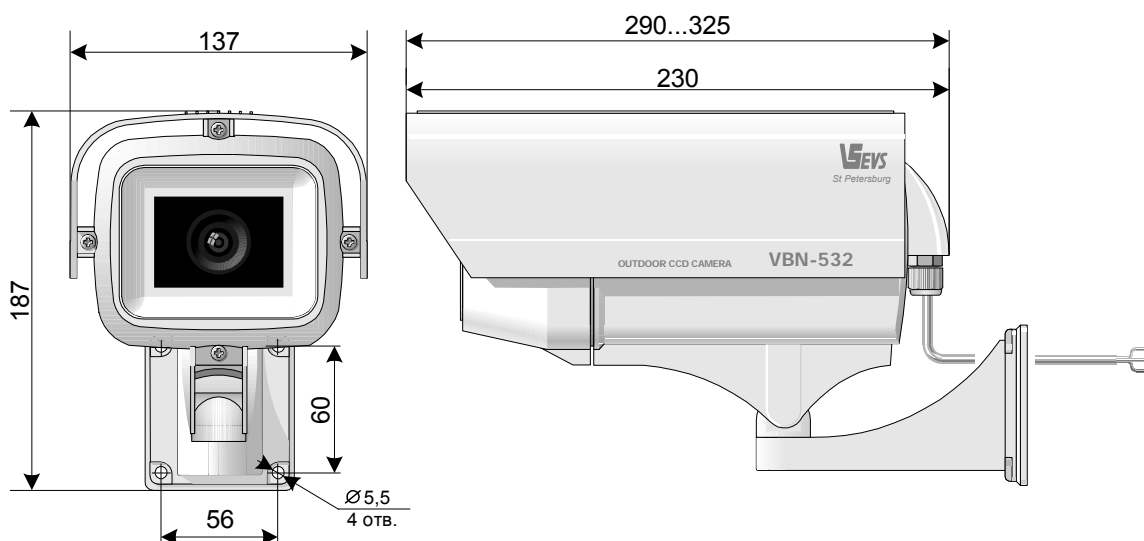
Камера VBN-532 в пластмассовом корпусе.
